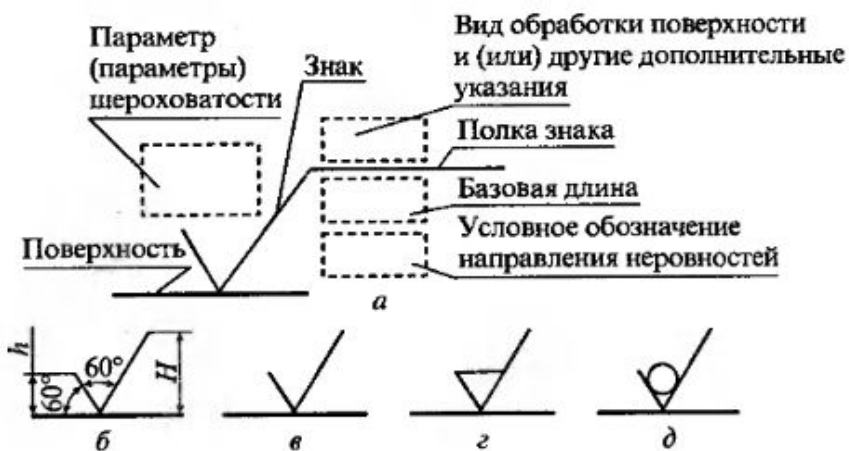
Структура и знаки обозначения шероховатости поверхности:
